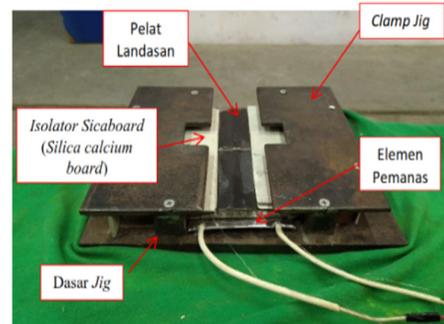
adalah skema instalasi penelitian *hot-gas welding* (HGW) untuk material HDPE sheet.
